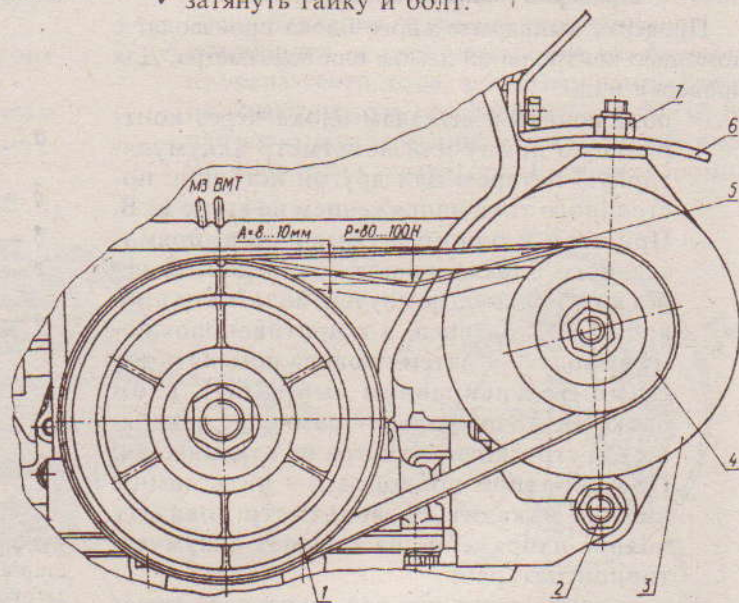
Привод генератора и проверка натяжения ремня: 1 - шкив коленчатого вала; 2 - гайка болта крепления генератора; 3 - генератор; 4 - шкив привода генератора; 5 - ремень; 6 - натяжная планка; 7 - гайка крепления генератора к натяжной планке
